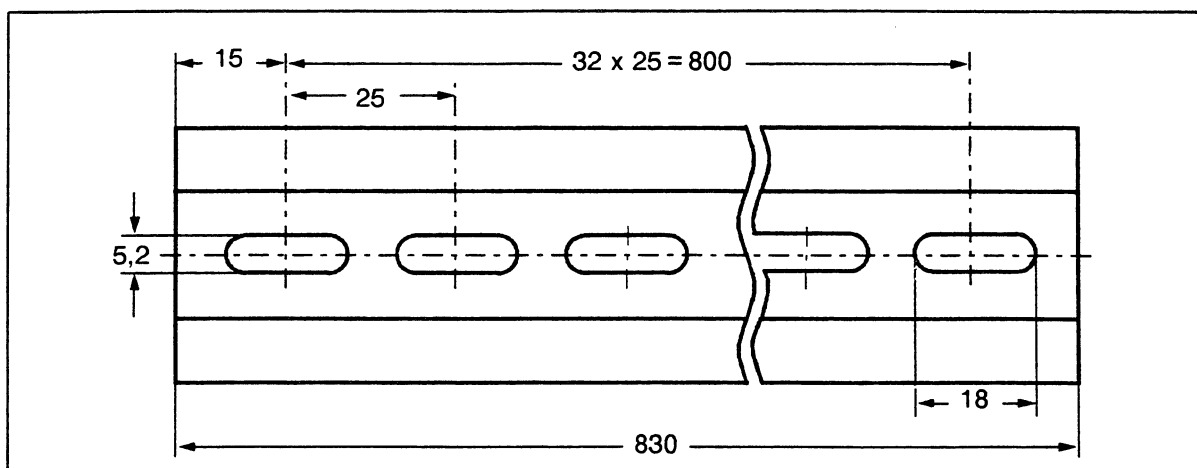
Plan d'encombrement du rail normalisé 830 mm
